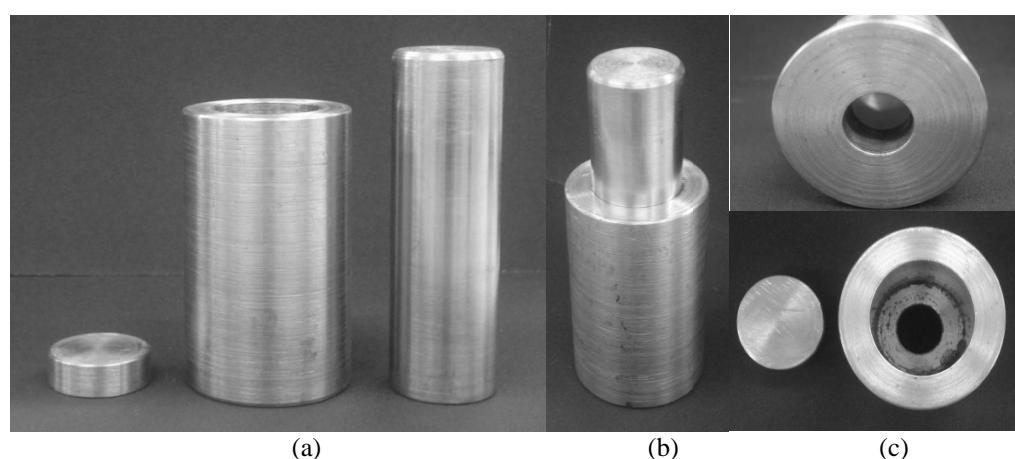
Dispositivo construído para ensaios de compressão. (a) vista frontal dos elementos separados (b) vista do dispositivo montado (c) vista superior do dispositivo e da pastilha e vista inferior.
